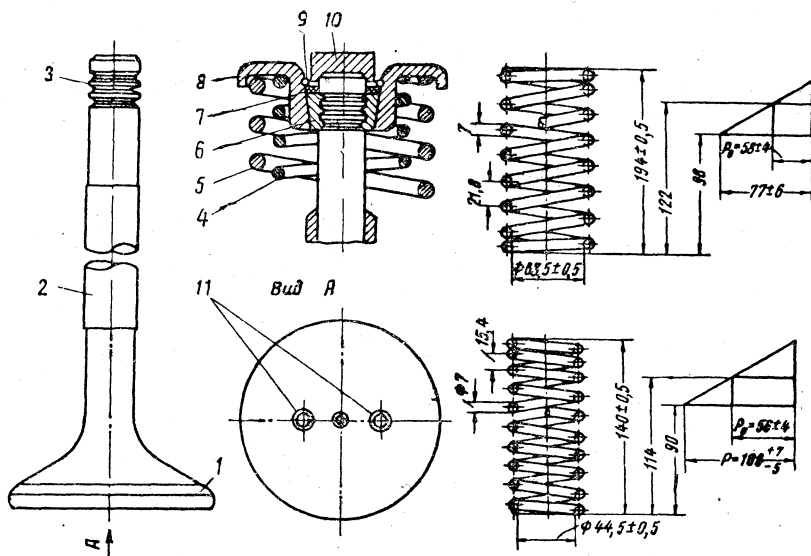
Впускные и выпускные клапаны цилиндровой крышки дизеля 2Д50:
